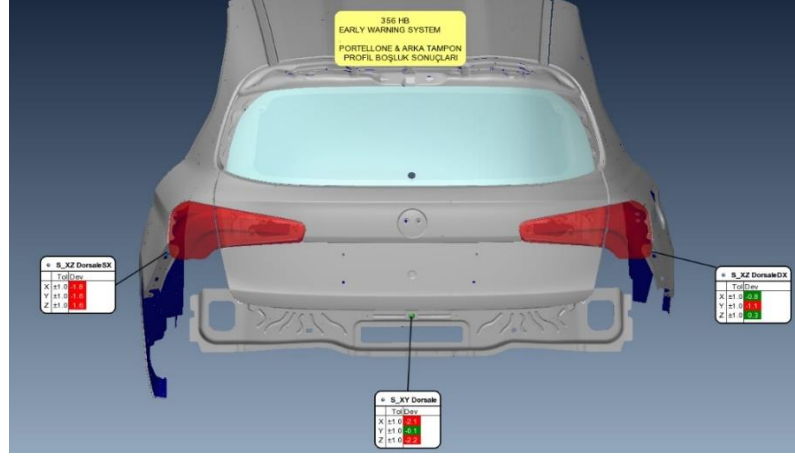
24. Egea Hatchback Bagaj kapağı double projesi
